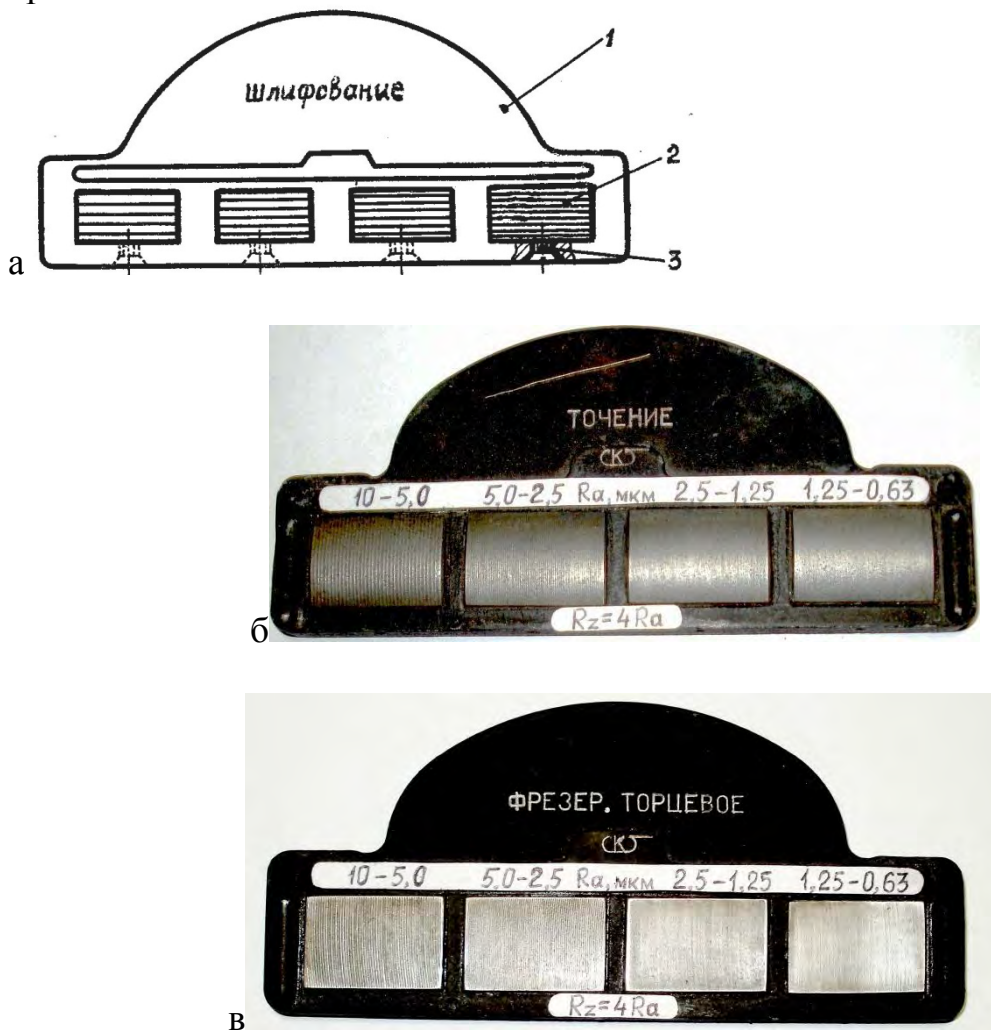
Образцы шероховатости поверхностей: а – устройство набора (1 – основание, 2 – образец, 3 – винт); б – набор для обработки точением (чугун); в – набор для торцевого фрезерования (сталь)
